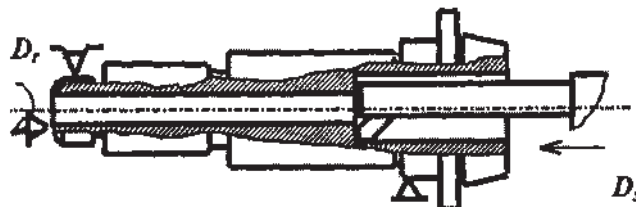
Схема обработки внутренних цилиндрических поверхностей
